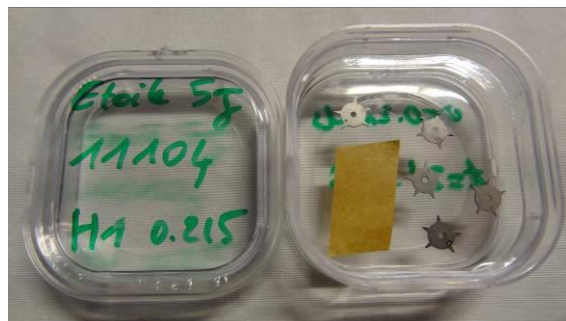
Vue macroscopique, v=0.2 mm/s.
